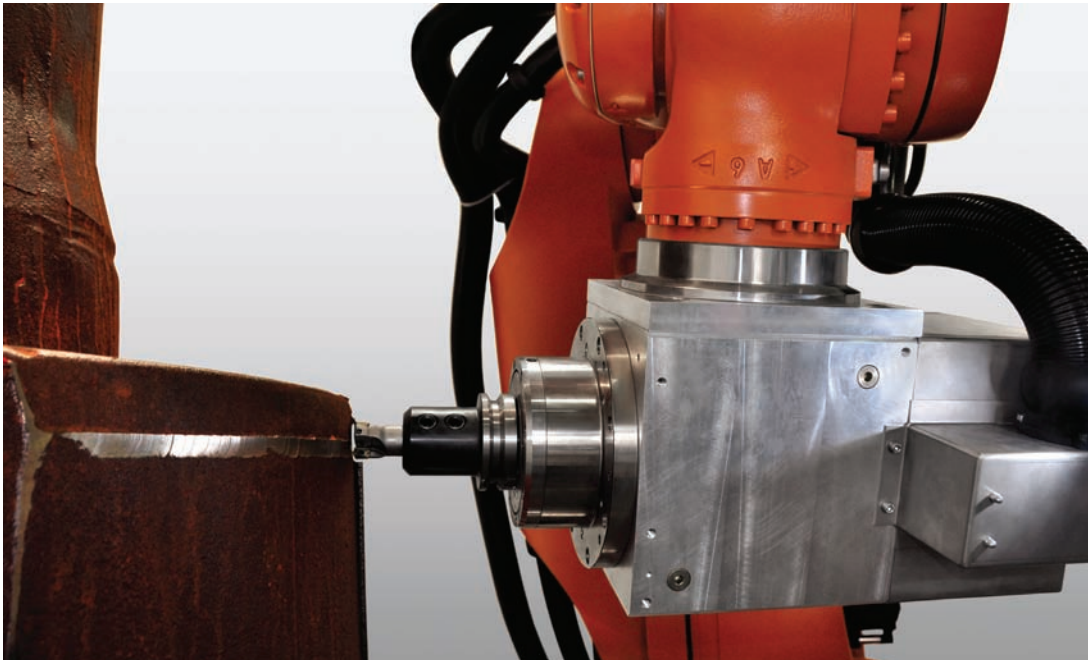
Bearbeiten des Gussteils mit adaptiven Bearbeitungsbahnen.
